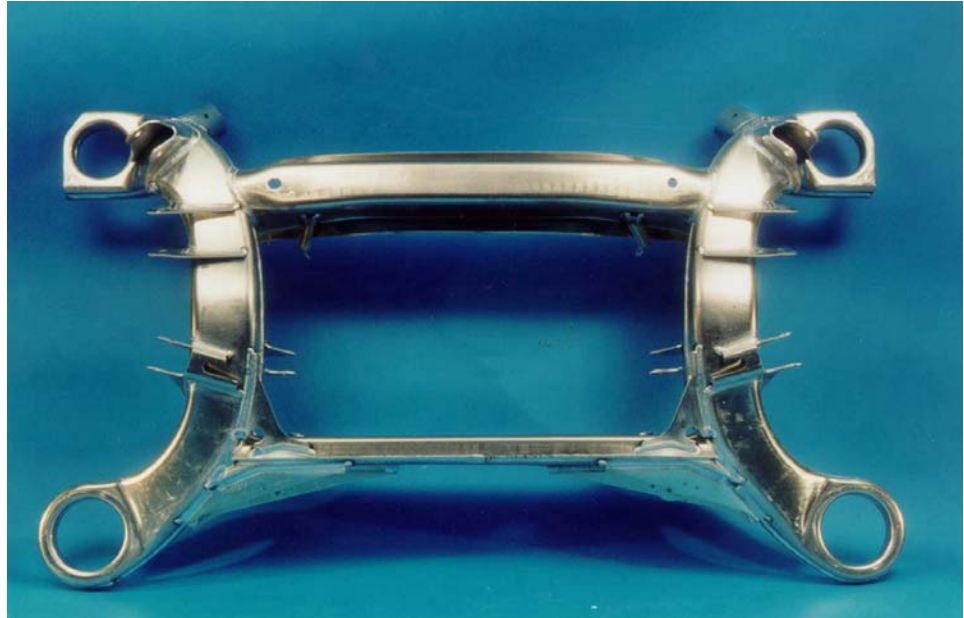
Geschweißter Hinterachsträger aus Aluminium (Mercedes W220)
